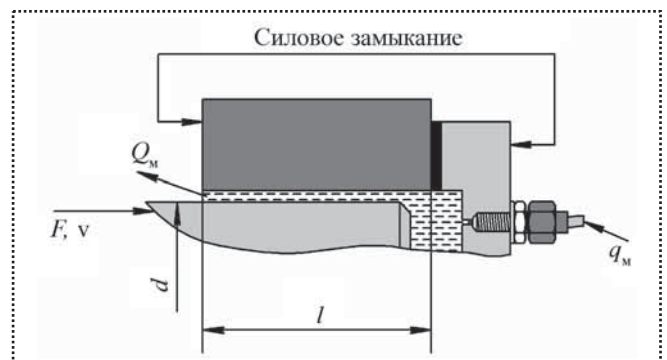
Схема гидропрессовой сборки при подводе масла с торца вала
